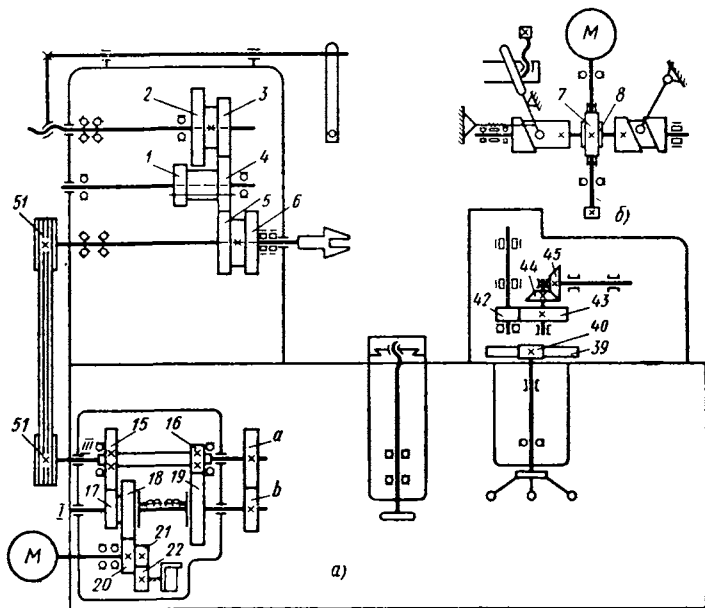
Кинематическая схема станка 1Н318Р (а); схема привода подачи прутка (б)
